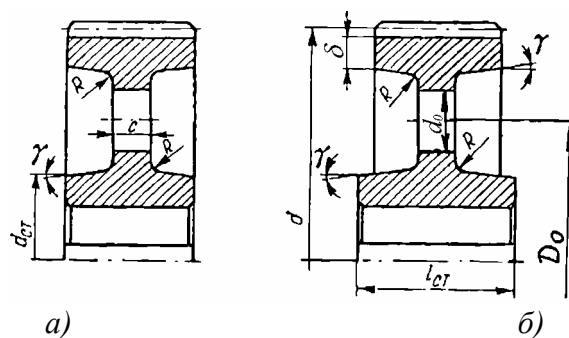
Конструкции штампованных цилиндрических зубчатых колес при двухсторонней штамповке
